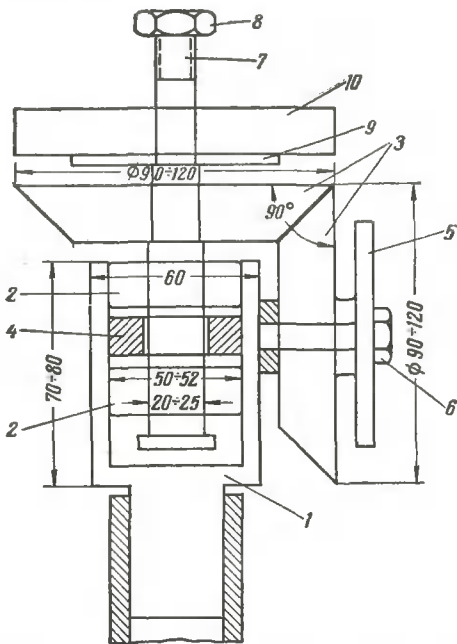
Поворотное устройство антенны; 1 — корпус; 2 — шарикоподшипники; 3 — конические шестерни; 4 — промежуточное кольцо; 5 — зубчатка; 6 — болт; 7 — поворотный вал; 8 — гайка для крепления бруса; 9 — упорный фланец; 10 — брус для крепления антенны;
